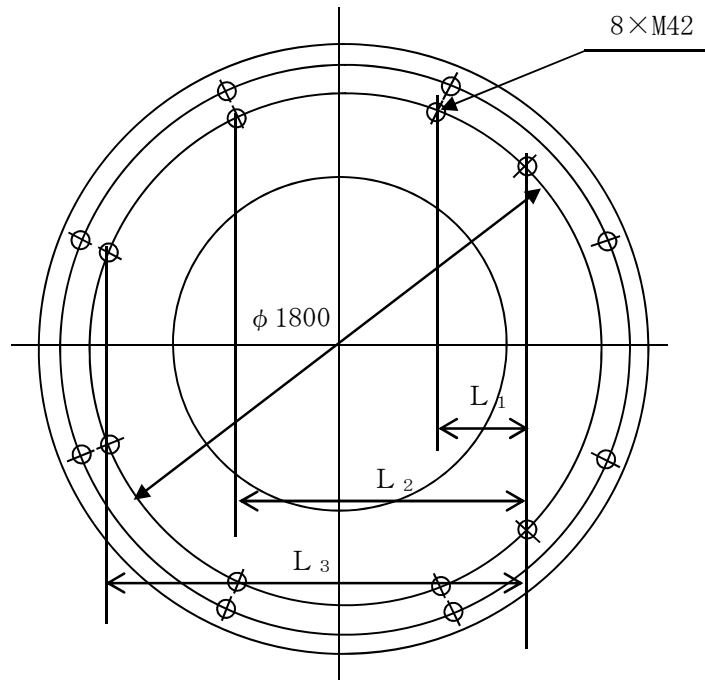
原動機台取付ボルトの各ボルト間寸法の配置図
